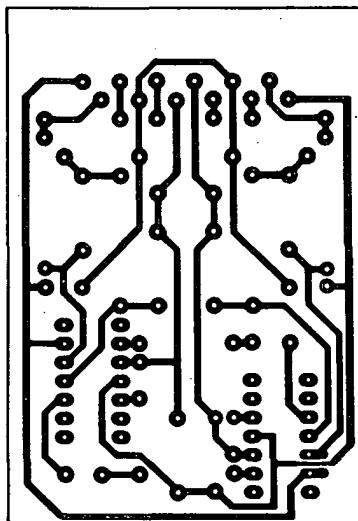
Deska s plošnými spoji oscilátoru (N27)
